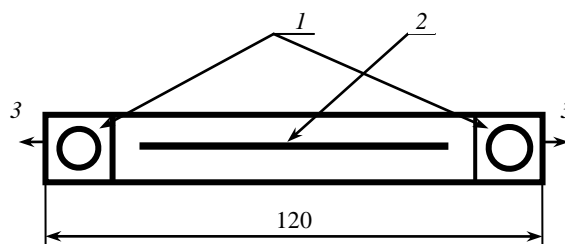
Образец для испытания на технологическую прочность: 1 — усилители с отверстием для фиксации образца в испытательной машине; 2 — сварной шов; 3 — направление скорости деформирования образца
